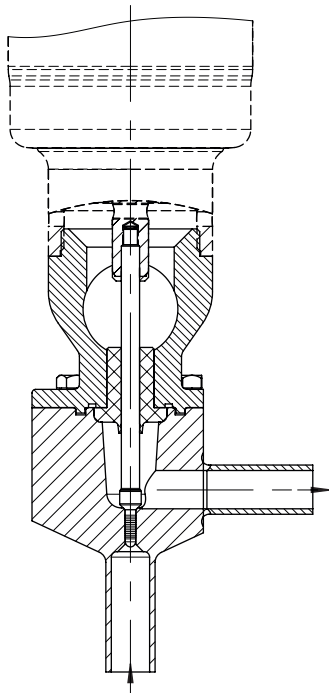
Stellventil Typ 3347/3379 mit Anschweißenden · Mikroventilausführung
